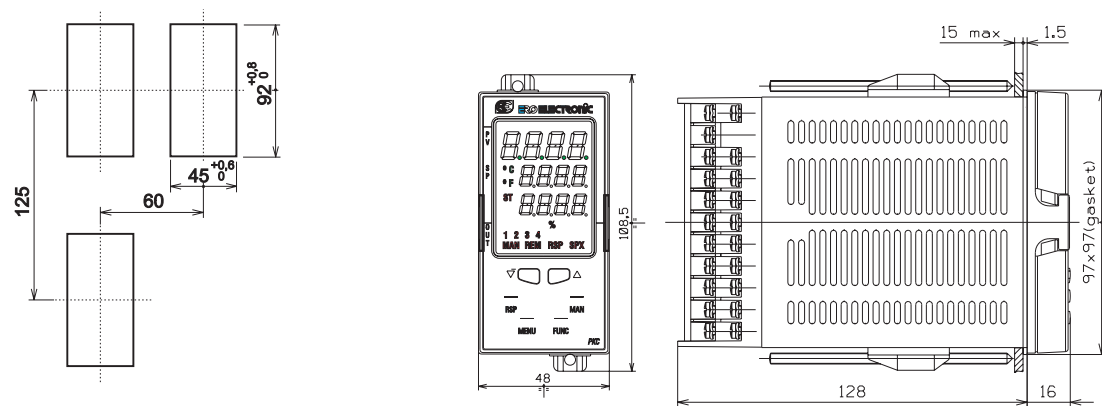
A DIMENSIONS ET PERCAGE POUR PKC
